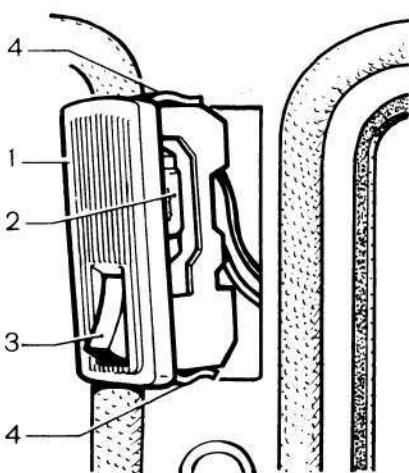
Плафон освещения салона: 1 — рассеиватель; 2 — лампа; 3 — выключатель; 4 — пружины крепления
